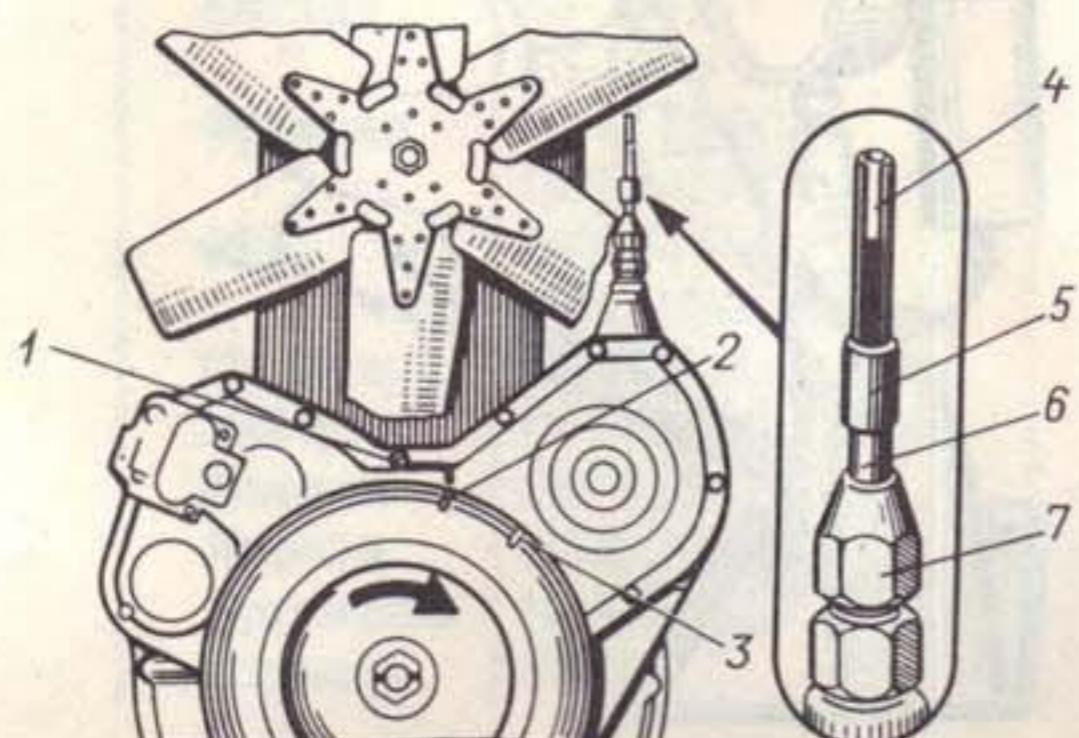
Проверка установочного угла опережения вспрыска топлива:
